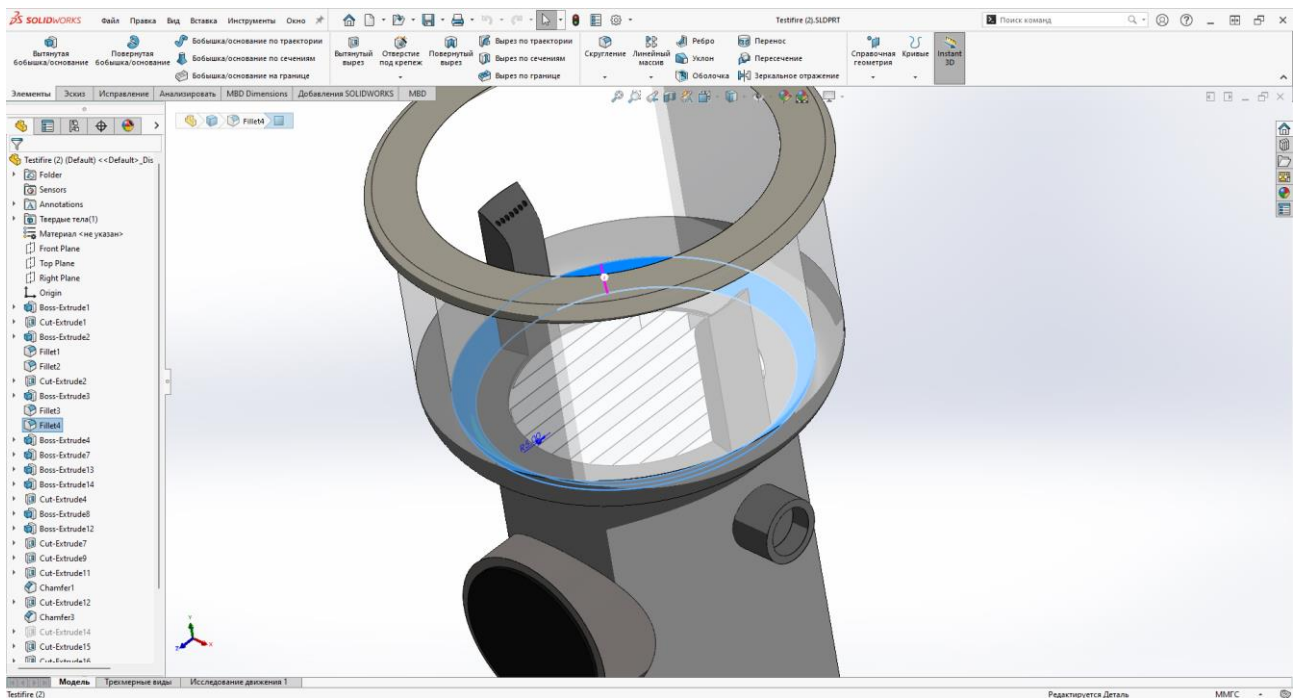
Змодельований корпус у середовищі SolidWorks
